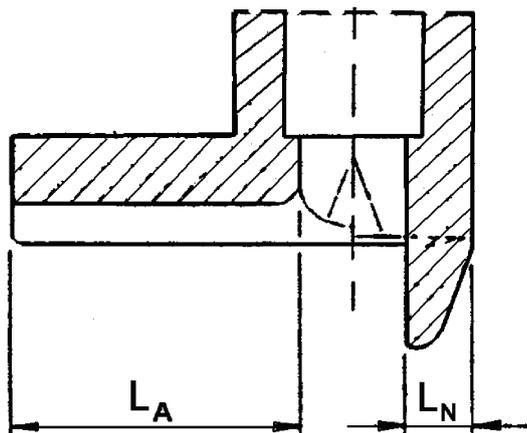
Mindestmaße an Schweißschuhen
